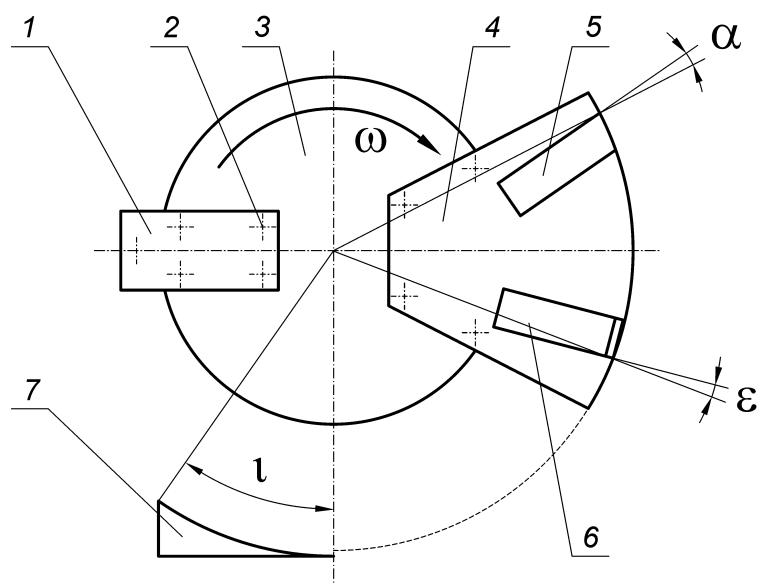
Схема к определению угла наклона лопатки к радиусу ротора α и угла охвата ротора выбросным порогом ι ; 1 – противовес; 2 – болтовое крепление; 3 – ротор; 4 – сектор; 5 – лопатка; 6 – нож; 7 – выбросной порог
